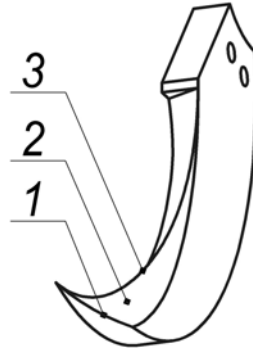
Зуб фрезерного робочого органа, поверхня якого виконана у вигляді торсу з ребром звороту:
